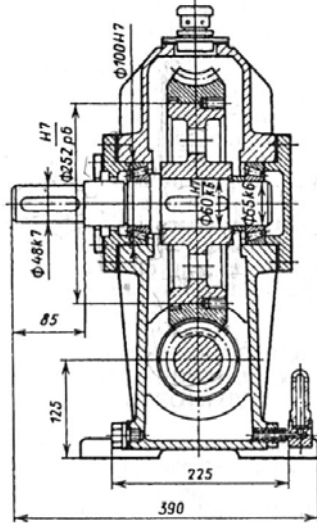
Одноступінчастий черв'ячний редуктор з нижнім розташуванням черв'яка
